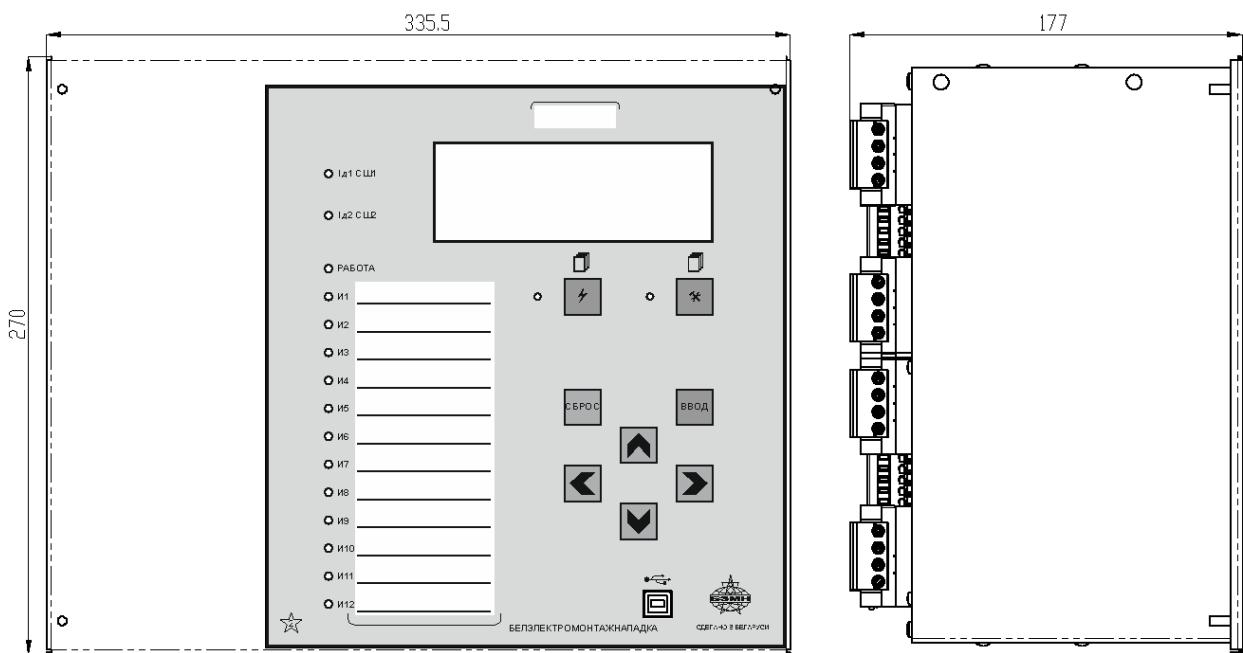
Габаритные размеры MP90x, корпус К3
